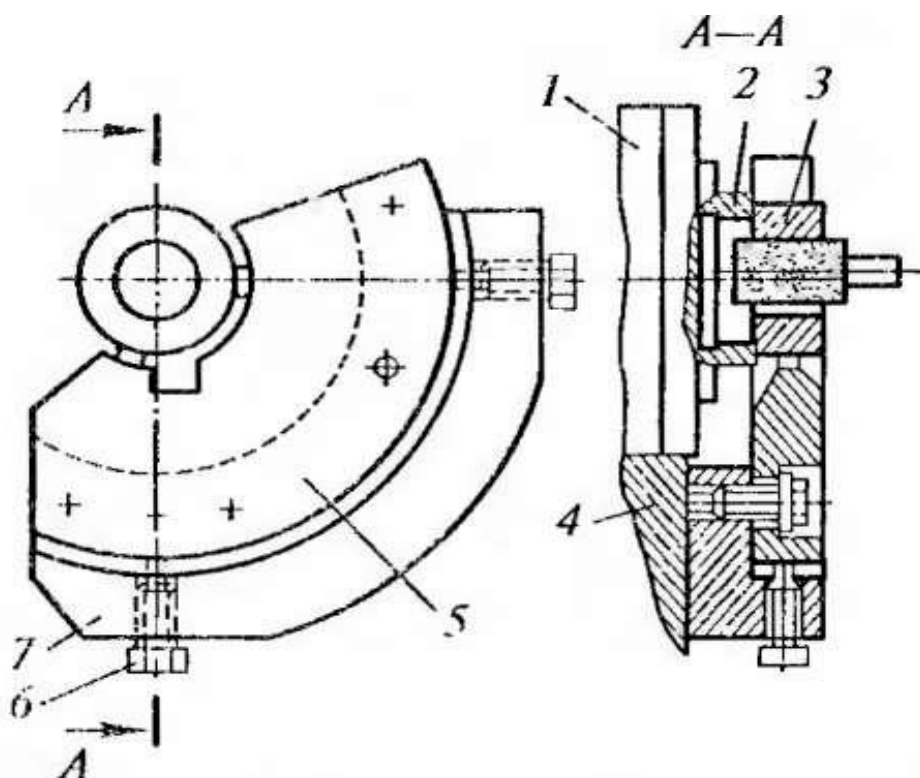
Приспособление на башмаках для базирования заготовки:
